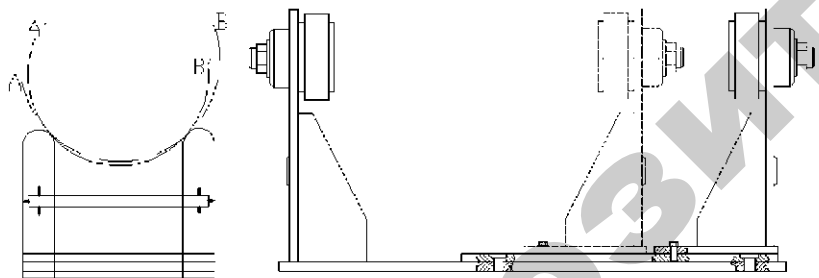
Приспособления для поворота статора или ротора вокруг горизонтальной оси
